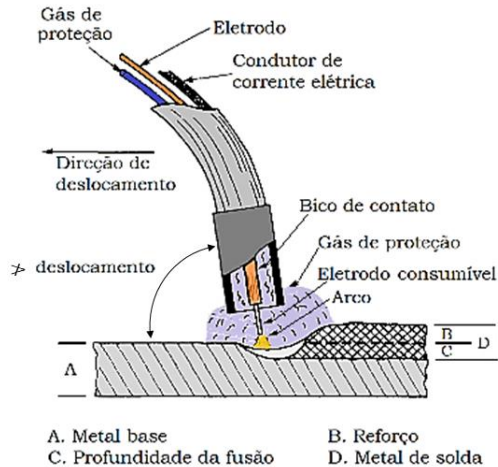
1 – Esquema do processo da soldagem MIG/MAG. [Adaptado de Linnert, 1994].
